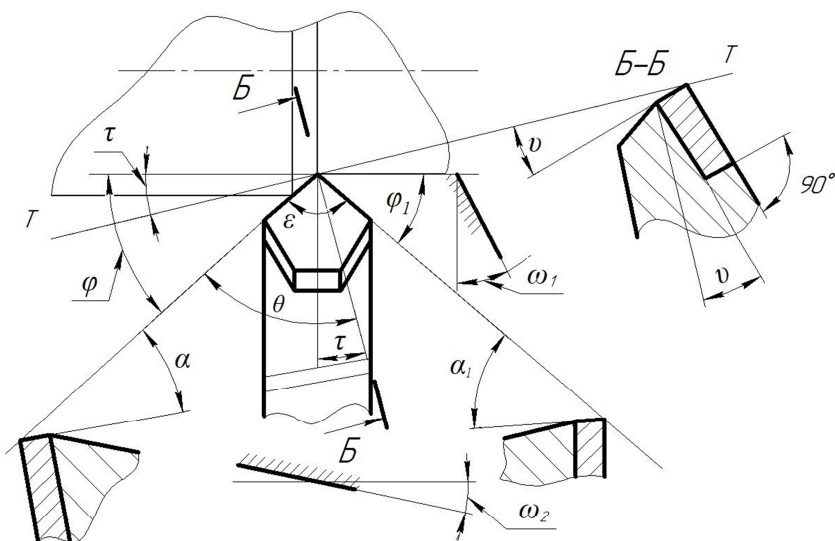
Схема расположения опорной поверхности пластины на державке резца
